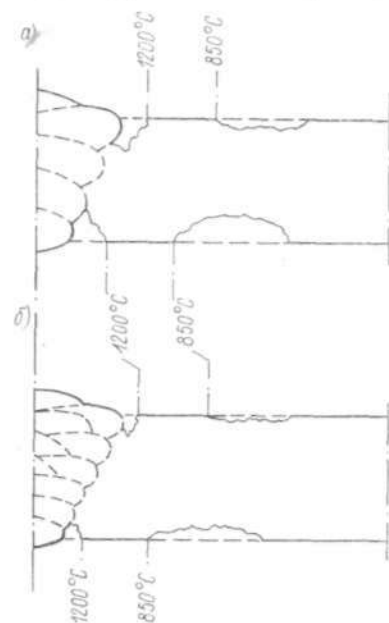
Схема коррозионного разрушения сварного соединения стали 1X18H10T в растворе азотной кислоты с хромпиком: а — сварка «толстыми» валиками без охлаждения; б — сварка «тонкими» валиками с охлаждением.
